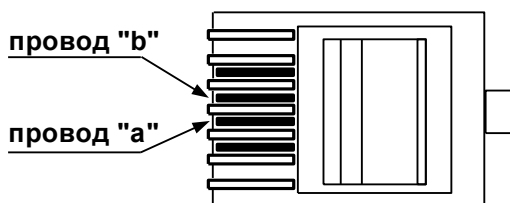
Схема монтажа проводов в вилке 5-0641335-3 AMP
